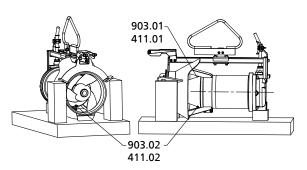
Drenaje del líquido lubricante; Amaline 300 con motor 86
